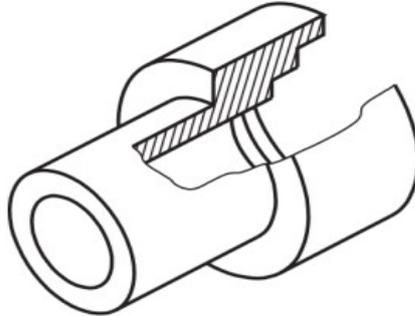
Exemplo de peça para aplicação do conteúdo de corte com rebatimento.
